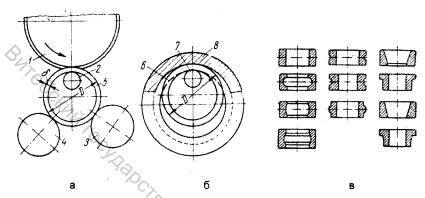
Схемы открытой (а), закрытой (б) раскатки и раскатанные заготовки (в); 1 – обжимной ролик; 2 – опорный ролик; 3, 4 – контрольные ролики; 5 – поковка; 6 – полая заготовка; 7 - опорный ролик; 8 – обжимное кольцо
